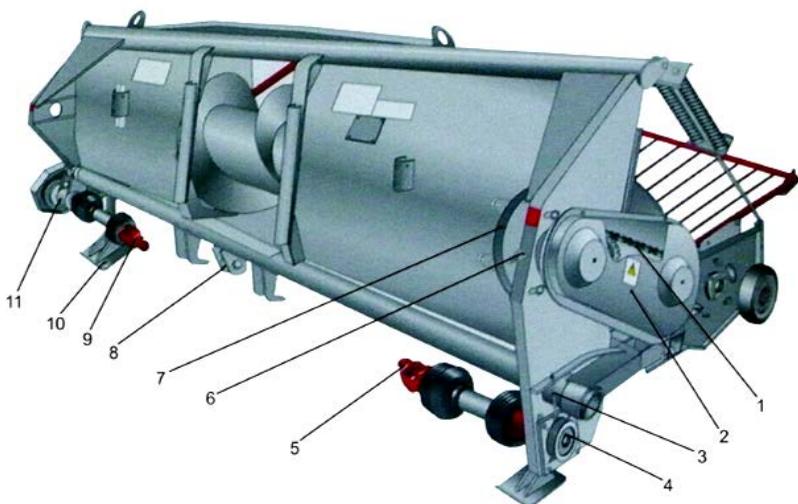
Платформа-подборщик (вид сзади): 1 – цепь привода шнека; 2 – правый рычаг шнека; 3 – винт натяжной цепи привода верхнего вала; 4 – нижний вал; 5 – вал карданный привода шнека платформы; 6 – натяжной винт цепи привода шнека; 7 – устройство предохранительное шнека платформы; 8 – шарнир соединения подборщика; 9 – вал карданный привода подборщика; 10 – левая опора установки платформы; 11 – контрпривод подборщика
